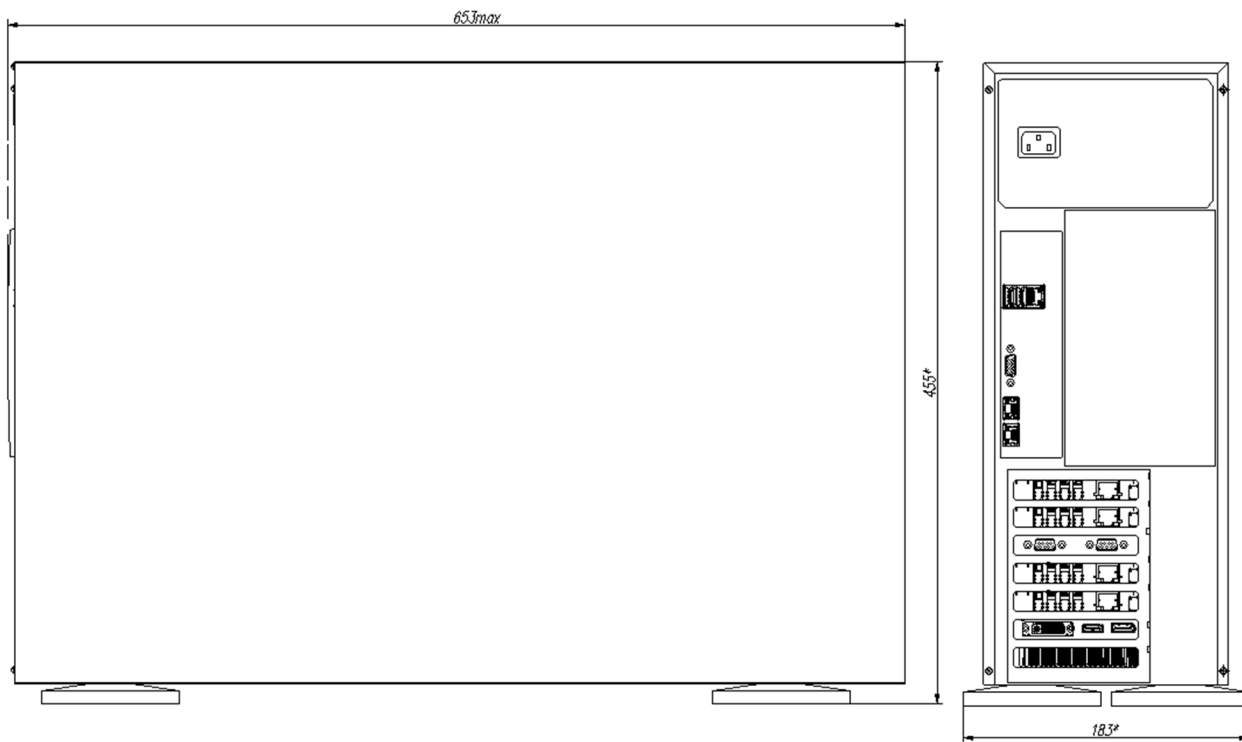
Габаритные размеры Блока в исполнении ЮФКВ.466531.005-01
